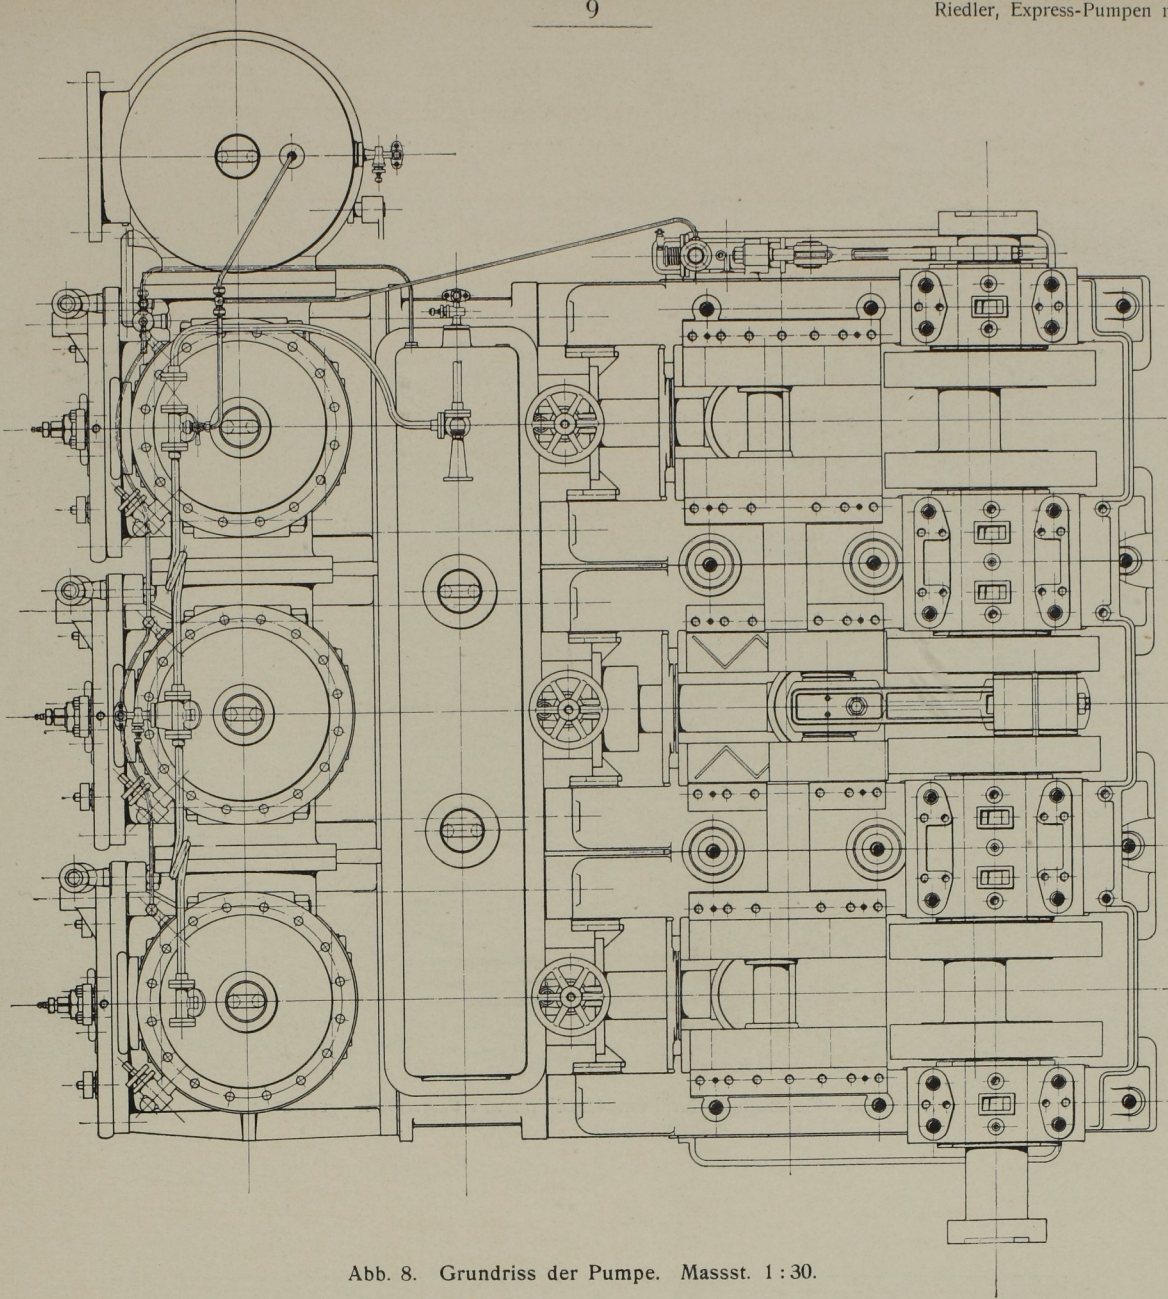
Grundriss der Pumpe. Massst. 1:30.
